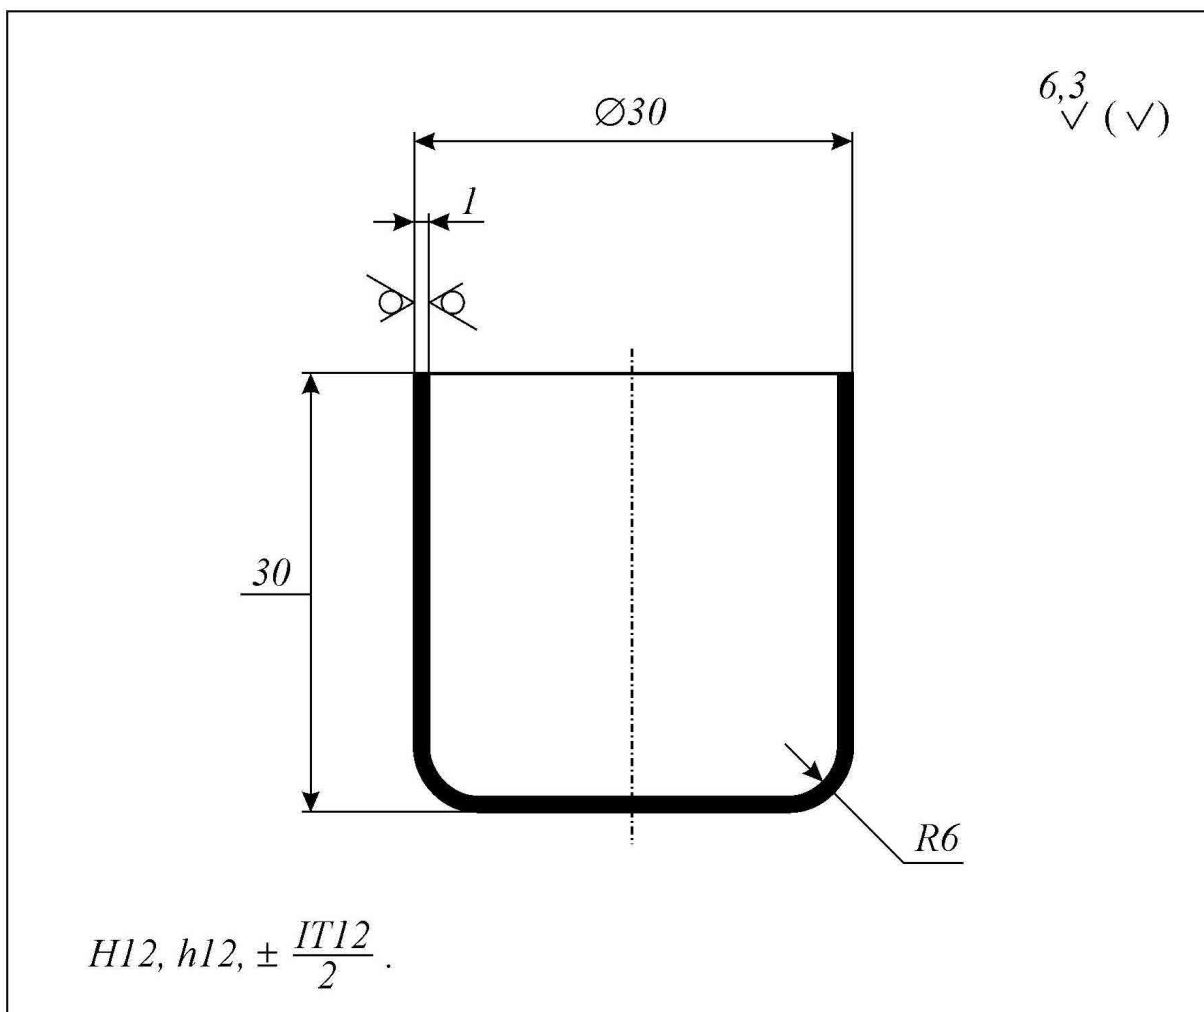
Кресленик деталі «Ковпачок»
